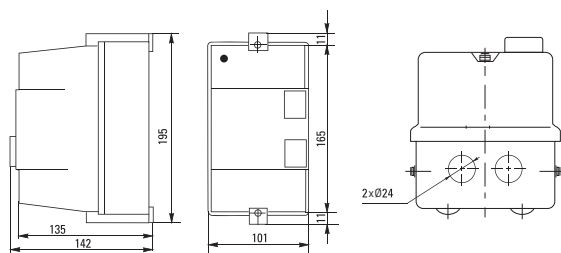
Габаритные размеры для ПМЛ 25-32А
